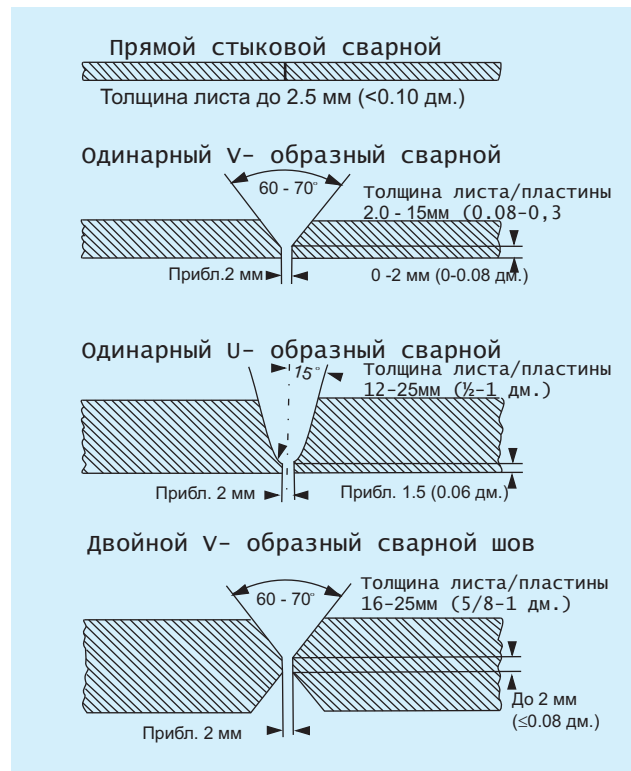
Подготовка кромок для сварки специальных нержавеющих сталей.
